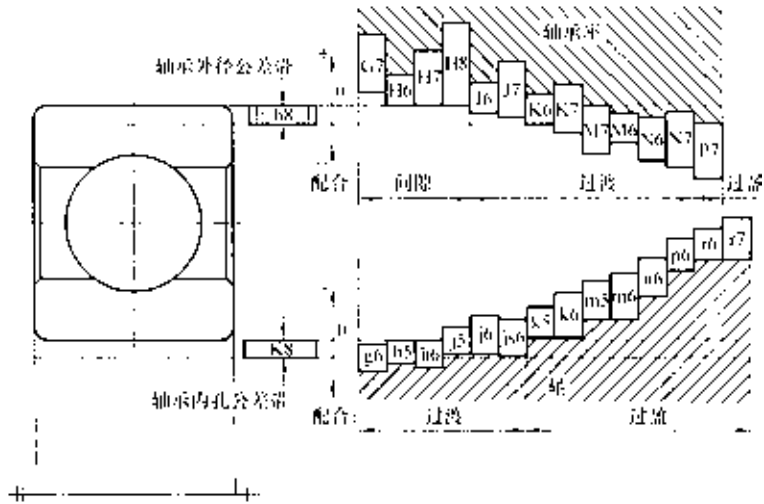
滚动轴承（P₀ 级公差）的配合
